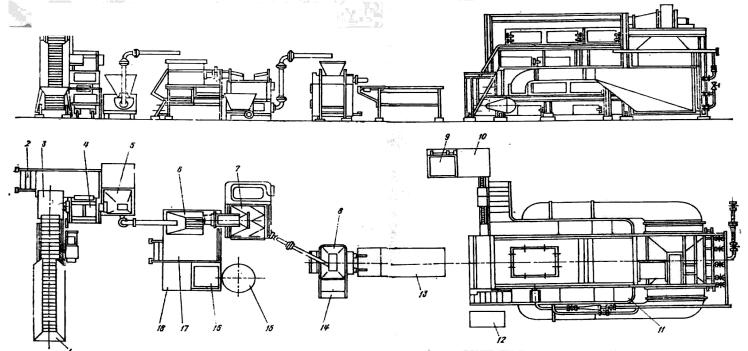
Линия производства фаршированной рыбы H2-ИТЛ-86: 1 — ковшовый конвейер; 2 - площадка; 3 - бункер; 4 - пресс-сепаратор; 5 - установка для транспортировки фарша; 6 - волчок; 7 - смеситель; 8 -шприц; 9, 16 - весы; 10, 13, 18 - столы; 11 — аппарат для теплообработки с охладителем; 12 - пульт управления; 14, 17 - площадки; 14 — дежа
